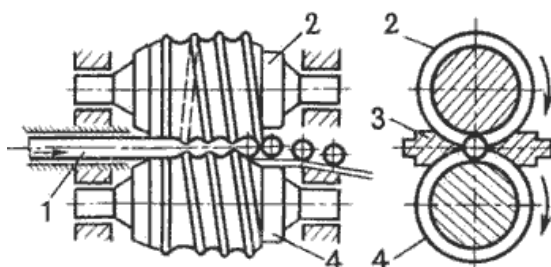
Схема прокатування кульок: 1 – вихідна заготовка, 2, 4 – прокатні валки, 3 – підтримуючі упори
